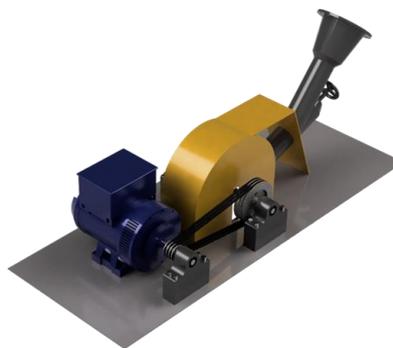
Assembly Turbin & Generator Tampak Samping
